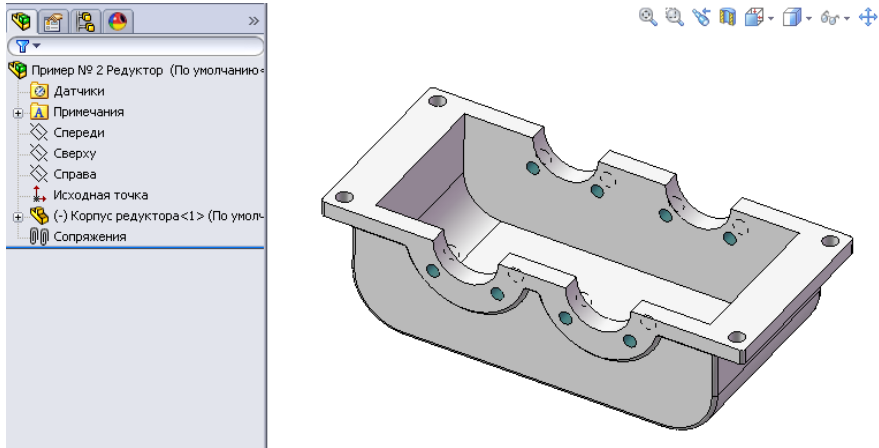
Перевернута деталь «Корпус редуктора» в складанні
